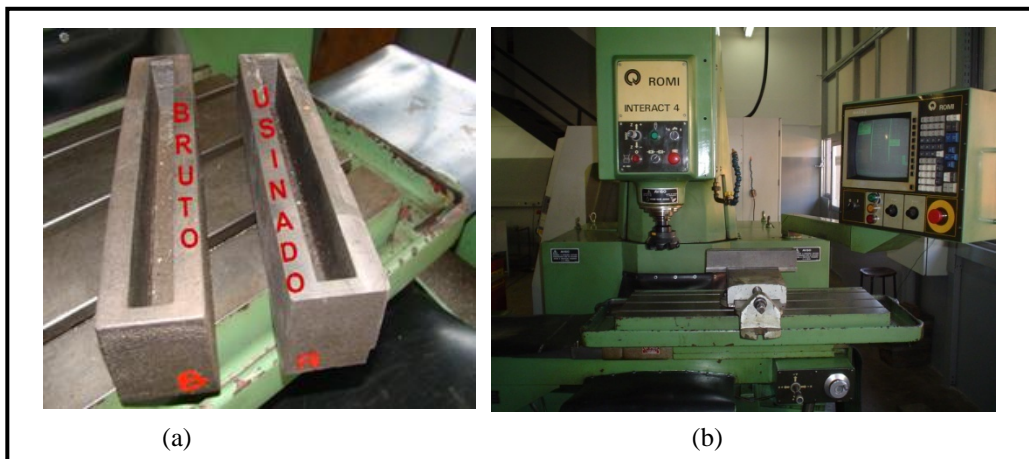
(a) corpo de prova bruto de fundição e pré-usinado; (b) fresadora com sistema de fixação do corpo prova através de morsa.
